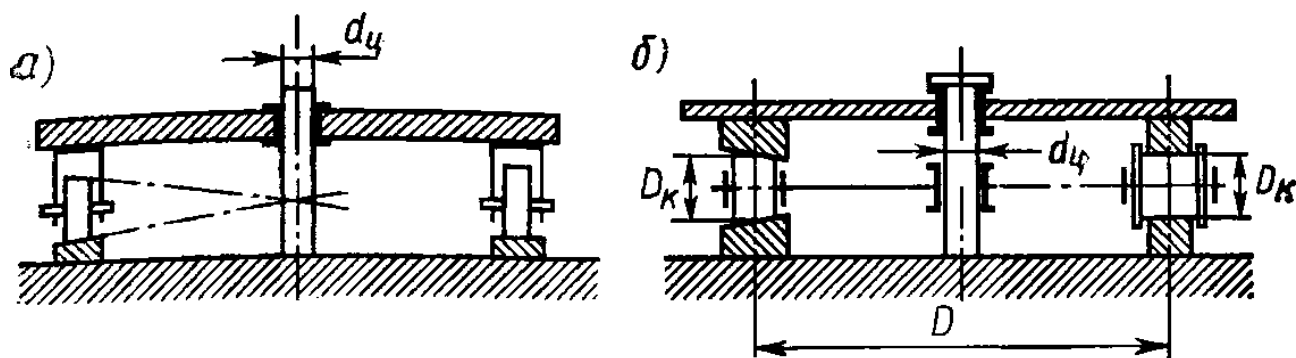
Опорно-поворотные устройства на поворотном круге:
